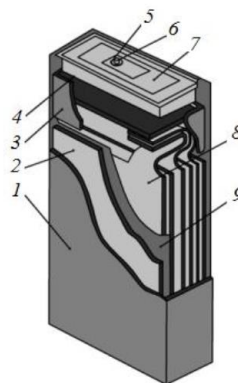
Конструкція Ni-MH акумулятора: 1 – корпус; 2 – негативний електрод; 3 – ізолятор; 4 – ізоляційна прокладка; 5 – ковпачок клапана; 6 – датчик тиску; 7 – кришка; 8 – позитивний електрод; 9 – сепаратор
